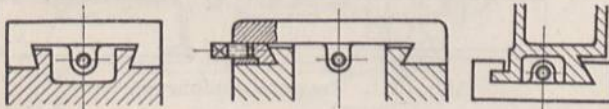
bis 1664. Schlittenführungen an Werkzeugmaschinen.
